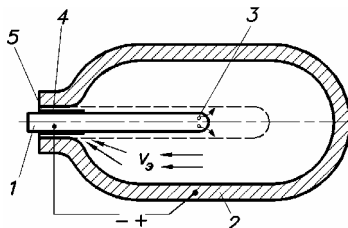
Схема обработки внутренней полости в заготовках, изготовленных из труднодеформируемых сплавов:
